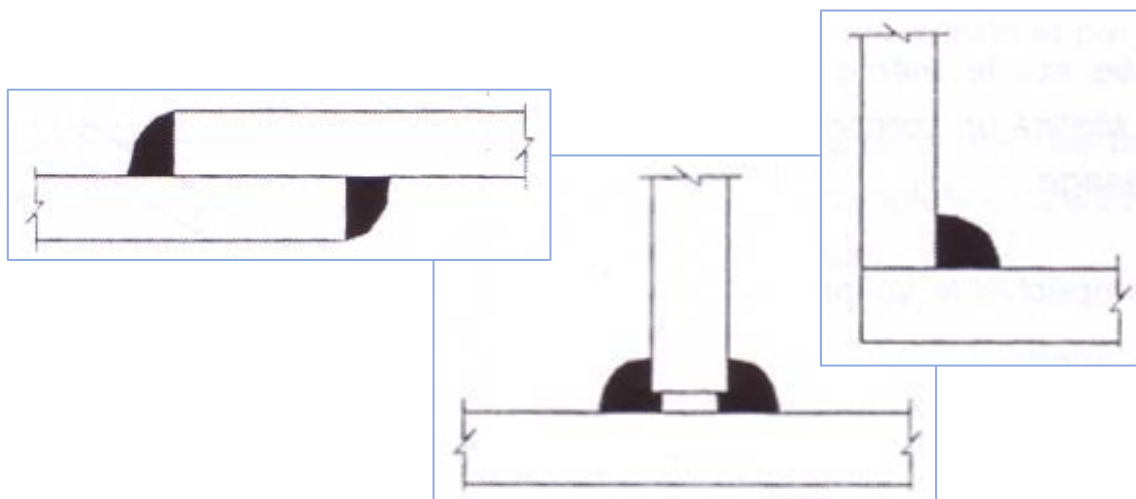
Schéma type de soudures d'angle (assemblage à recouvrement, assemblage en T, assemblage d'angle) [47]
